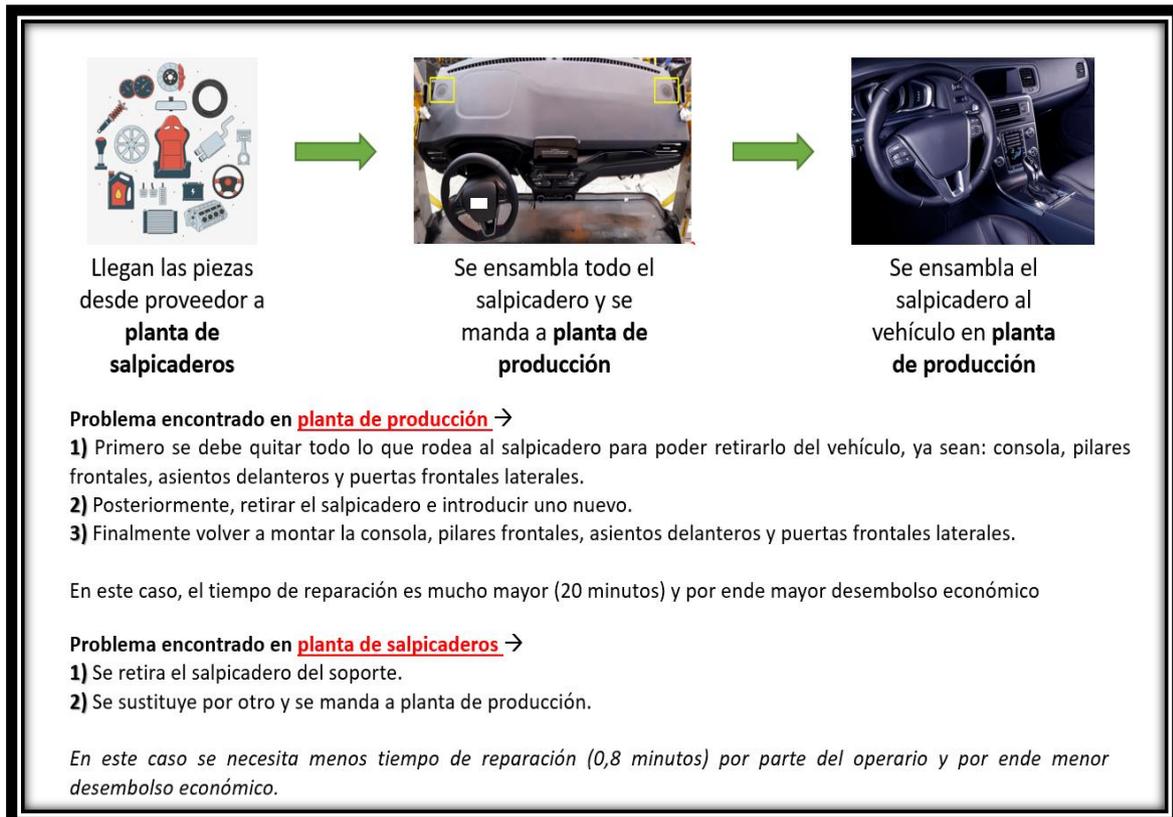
Esquema del montaje del salpicadero y los problemas encontrados en planta de producción y de salpicaderos
